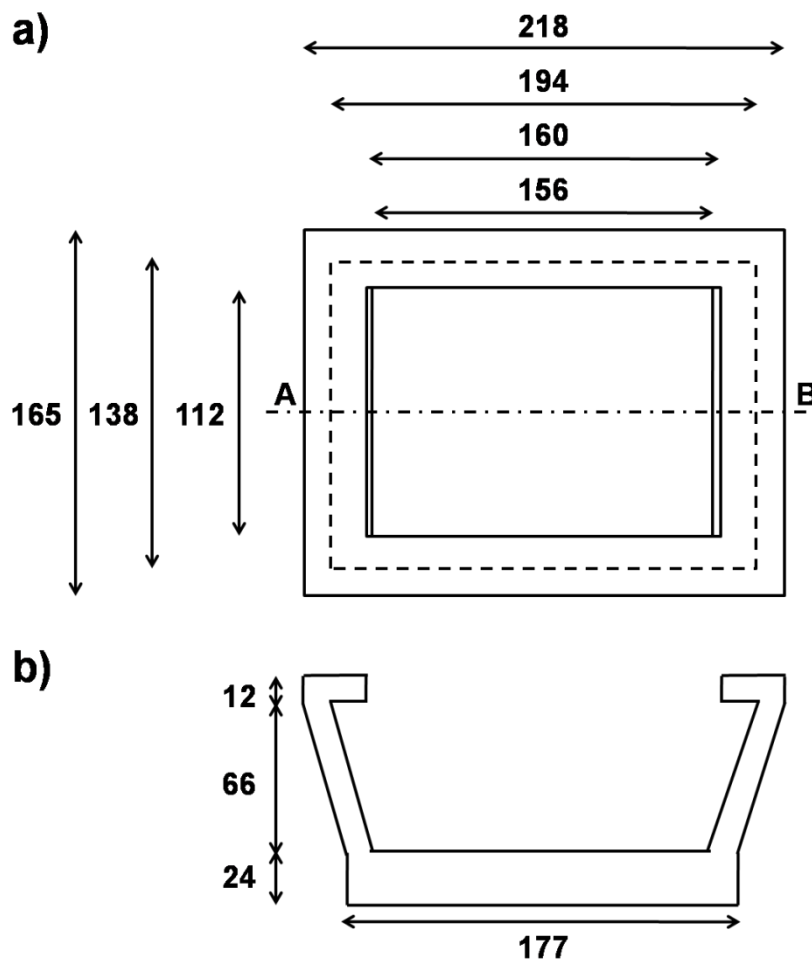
Geometría y dimensiones del IT-A (mm): a) Vista superior, b) Vista frontal.
